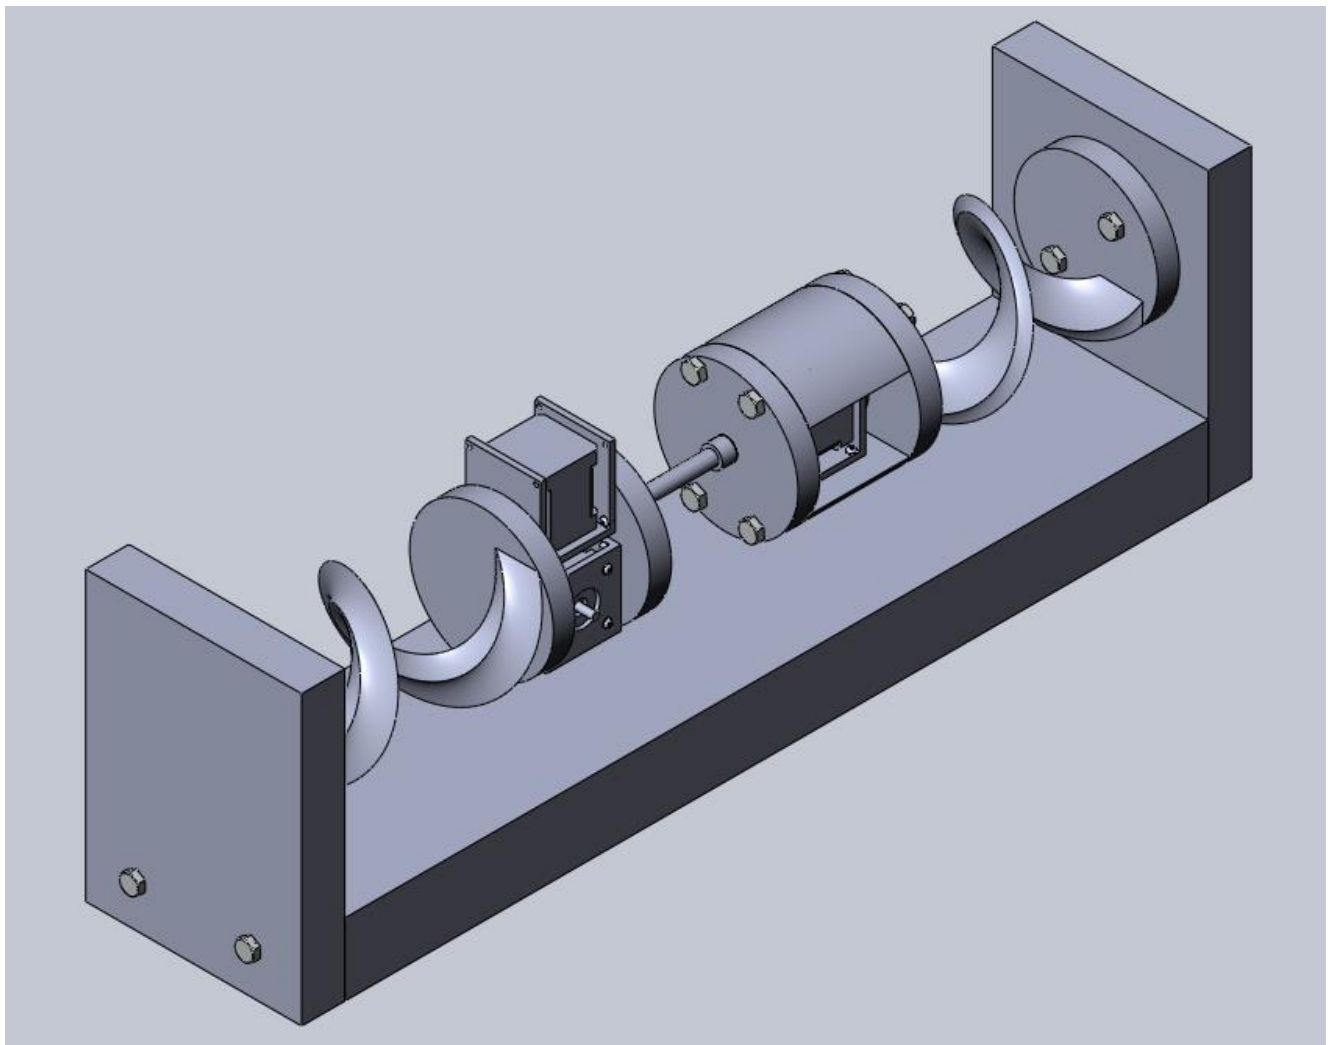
Ізометричний вигляд 3D-моделі стенда
